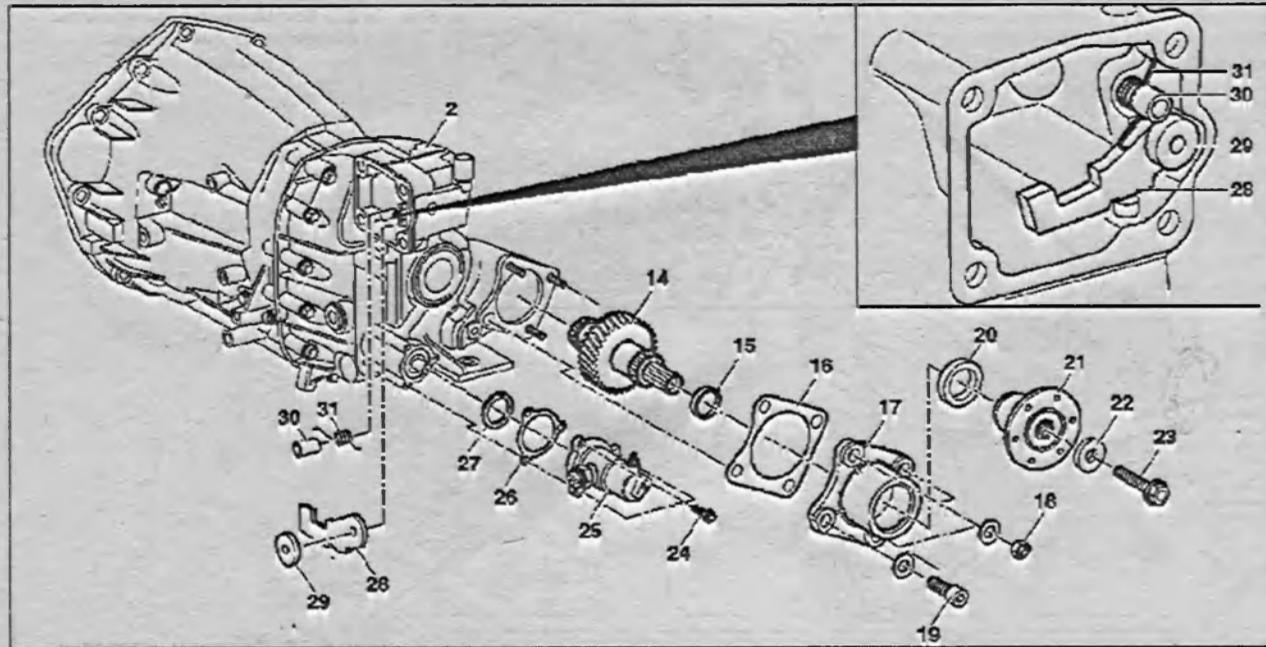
Разборка и сборка корпуса МКПП 711.620/621 с КОМ:
